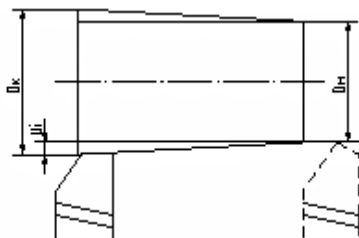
Погрешность формы заготовки (конусность) как следствие размерного износа резца
